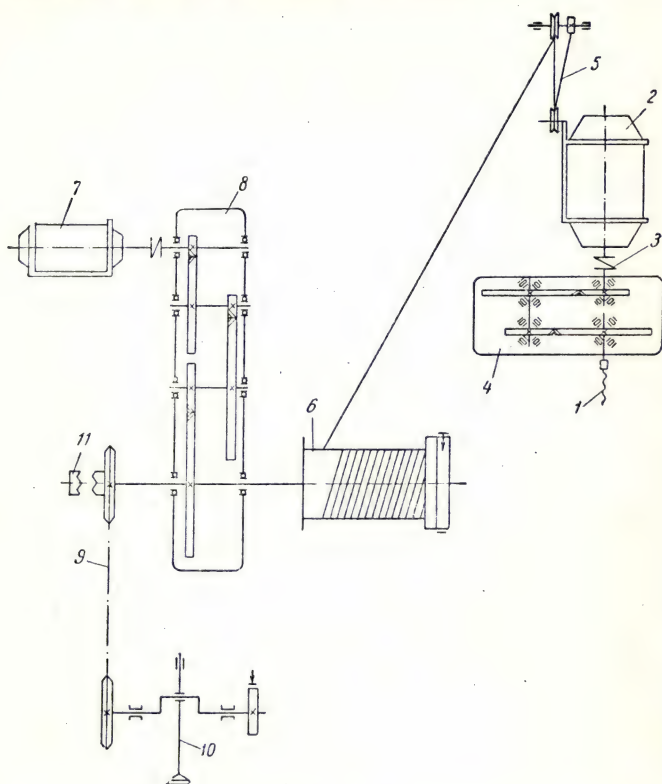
Кинематическая схема буровой установки БС-110/25м
